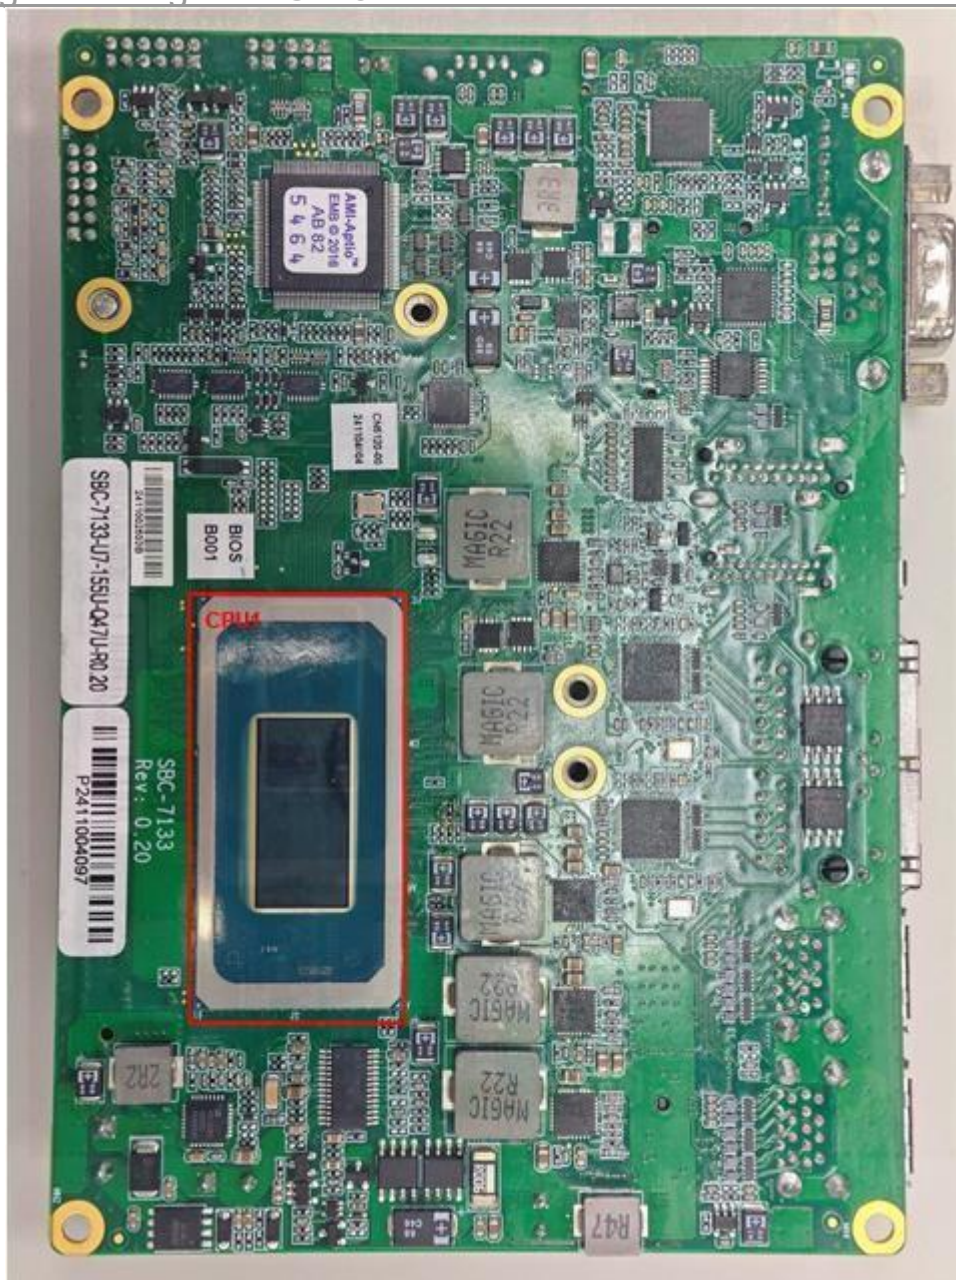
Position der Jumper und Anschlüsse – Unterseite des Mainboards
